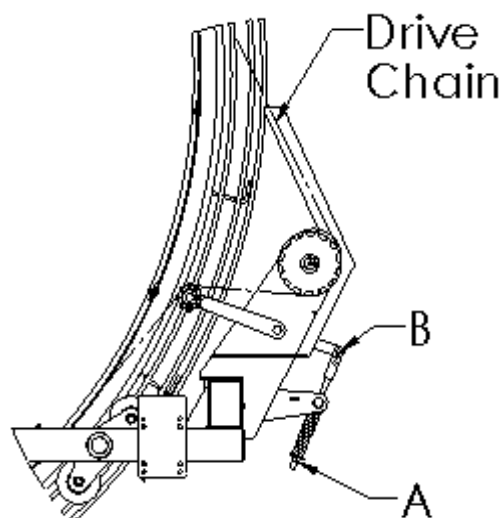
Регулировка напряжения цепи колеса привода
